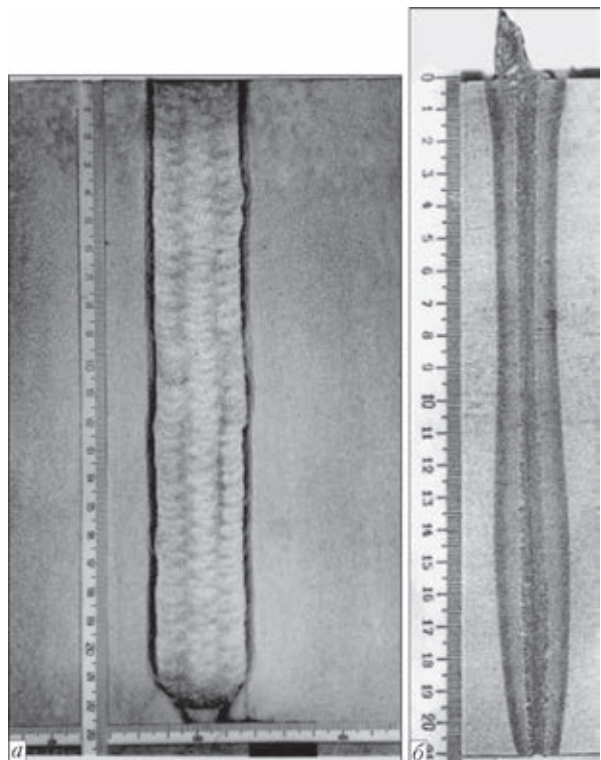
Макрошлифы поперечного сечения кольцевых швов низколегированной стали большой толщины, выполненных многослойной дуговой сваркой под флюсом (а) и однопроходной ЭЛС (б)
